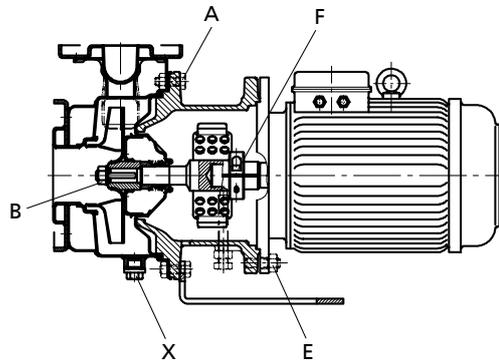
Schraubenanzugstellen für Etachrom B 050-025-125.1, 050-025-125, 050-025-160, 050-025-200, 050-032-125.1, 050-032-125, 050-032-160, 050-032-200, 065-040-125, 065-040-160, 065-040-200, 065-050-125, 065-050-160
